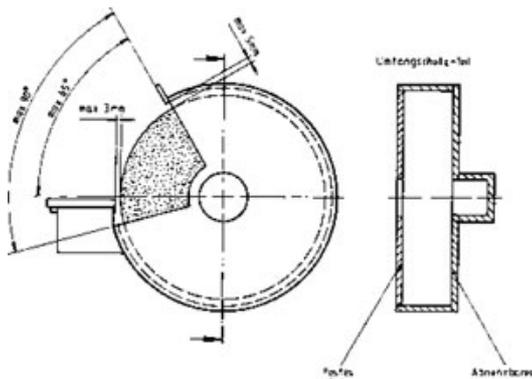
Prinzipskizze einer Schutzhaube für Ständerschleifmaschinen für das Umfangschleifen mit $v_s \leq 50$ m/s
